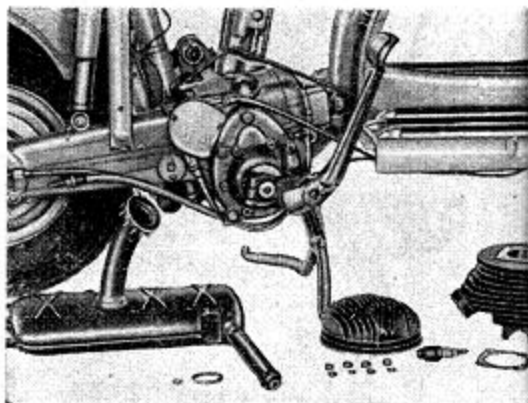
Desmontaje de cilindro, caño del escape y silenciador
